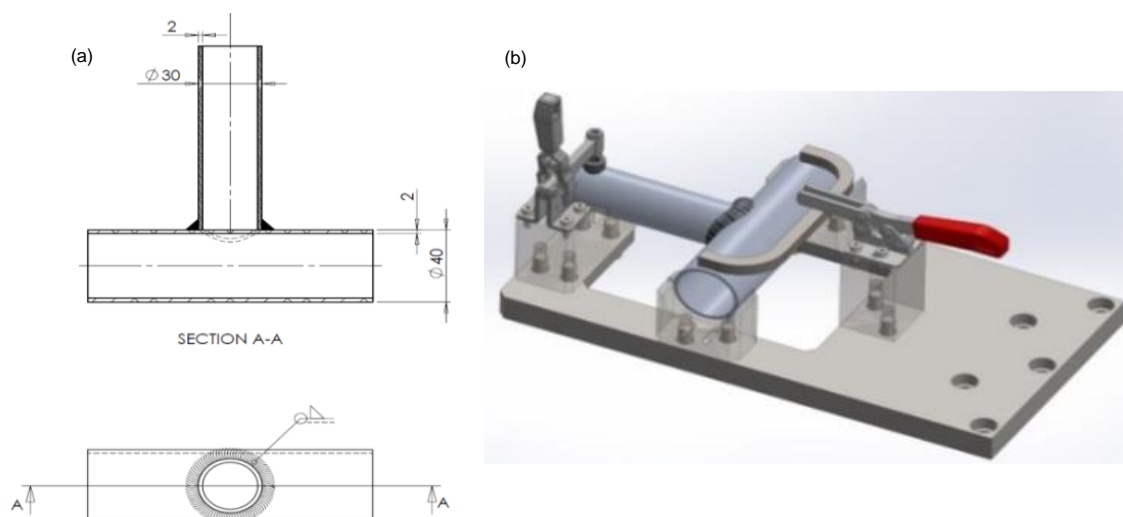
Ilustração da junta de soldadura (a) e do gabari de fixação dos tubos a soldar (b).
